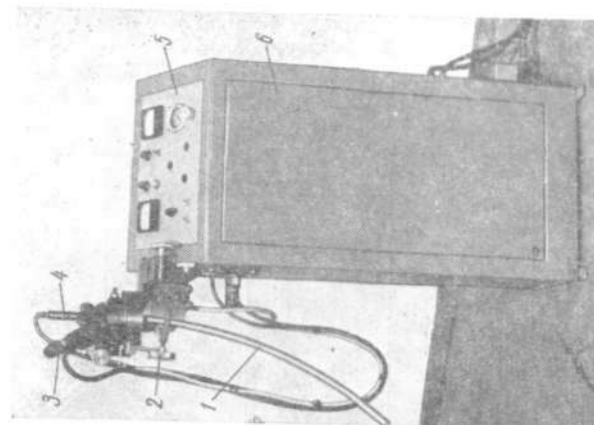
Автомат АДГ для сварки угловых соединений труб с арматурой.
